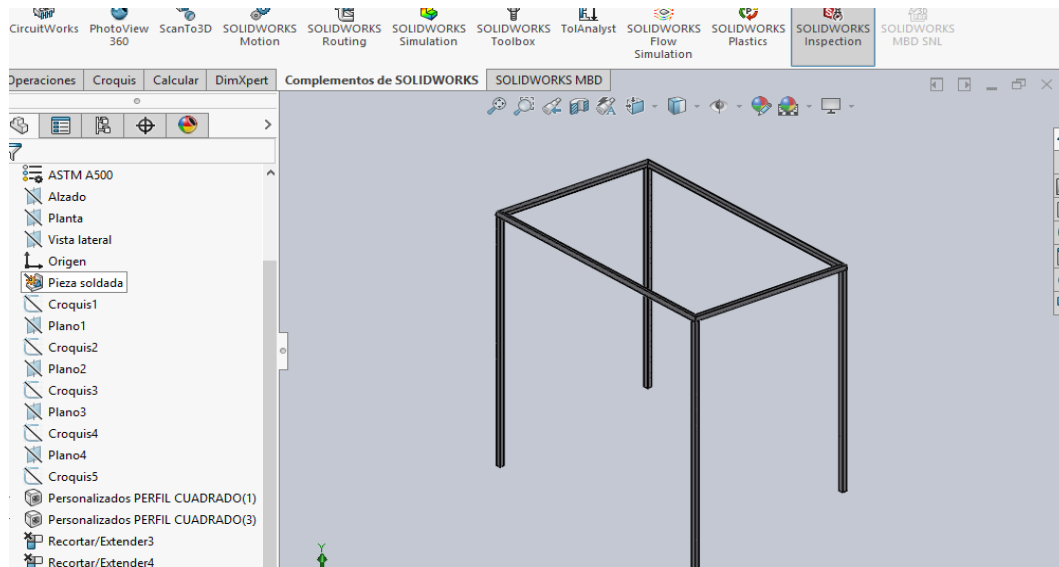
Modelado de la estructura y aplicación del perfil estructural
